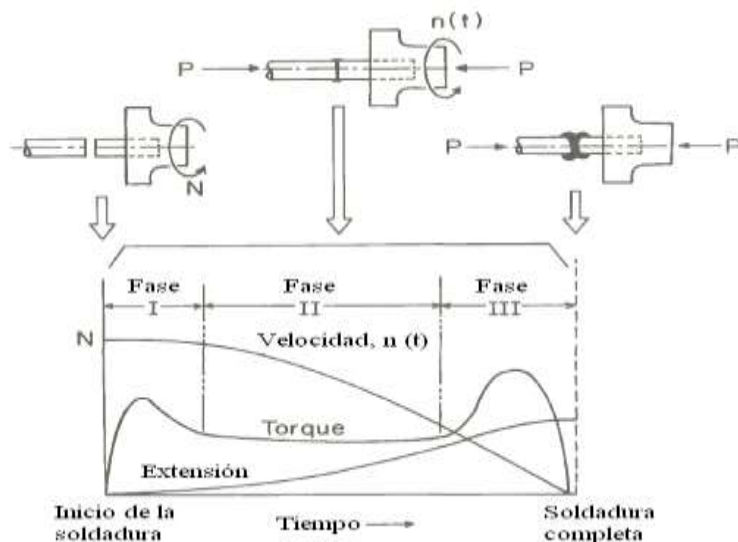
Soldadura por fricción rotativa. Fuente: Oberle *et al.* (1967).
